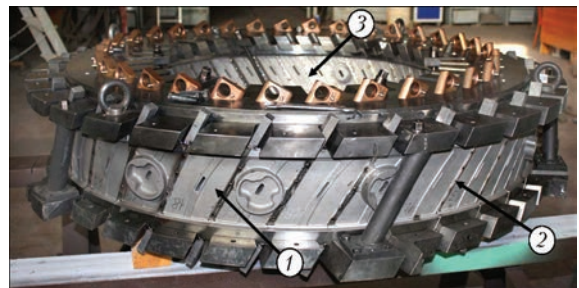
Внешний вид наружной части переднего корпуса КСД в сборочно-сварочном приспособлении: 1 — стойки; 2 — наружные стыки между стойками; 3 — внутренние стыки между стойками
